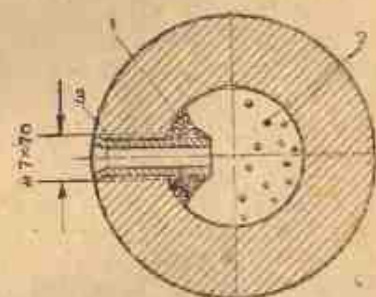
Перерезный разрез шейки коленчатого вала по масляной трубе.
